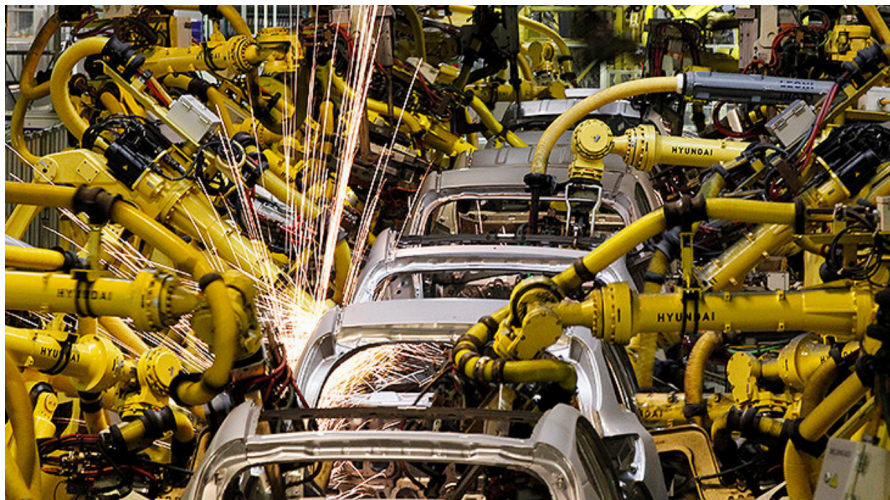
Cadena de soldadura sector automovilístico. [31]
